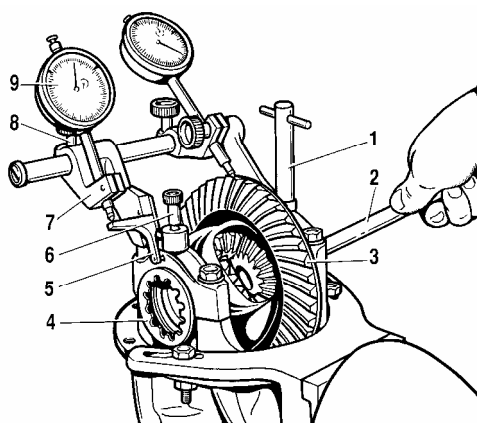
Проверка предварительного натяга подшипников коробки дифференциала приспособлением А.95688/Р:
